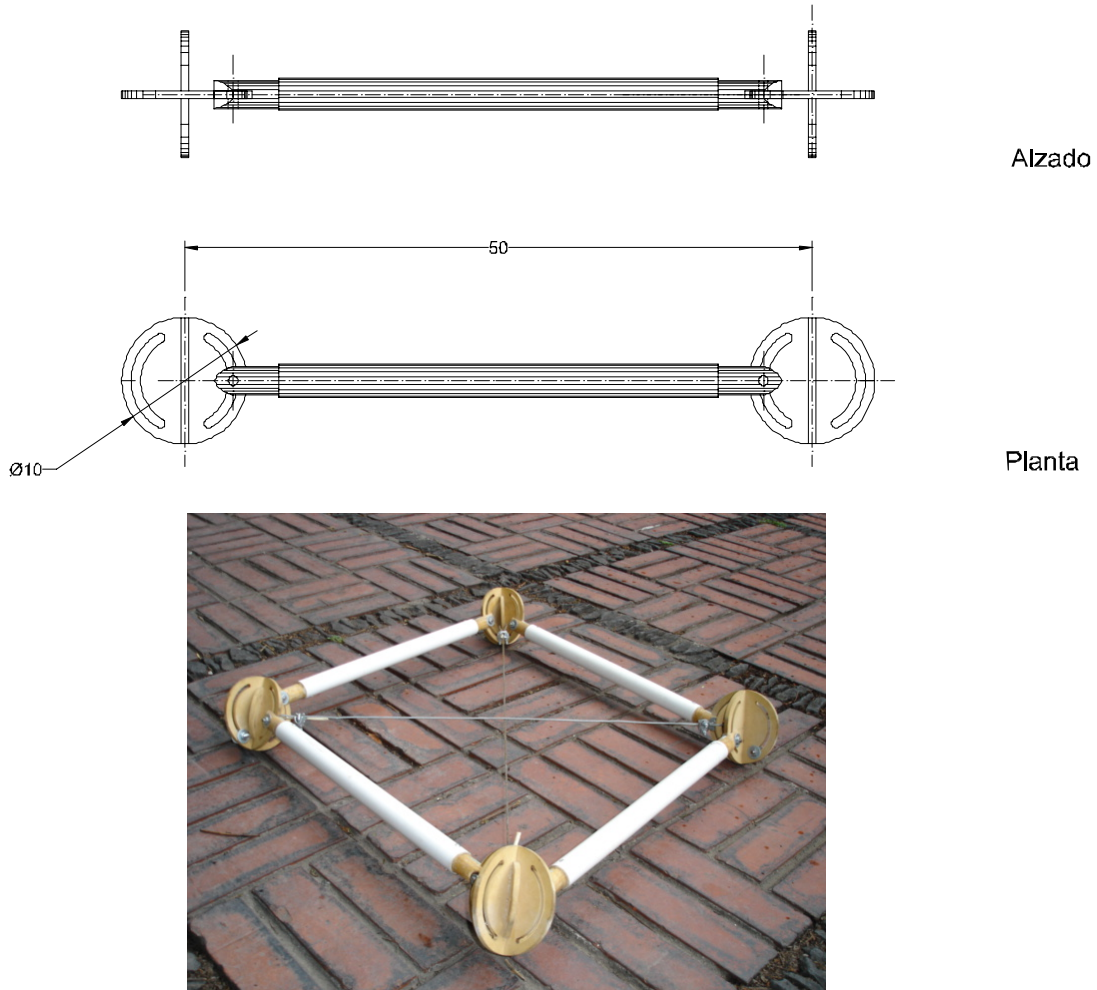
Sistema para construir el primer modelo de la estructura escala 1:1 compuesto por un nodo, un conector de madera, una barra de PVC y contraventeos con cables de acero.
